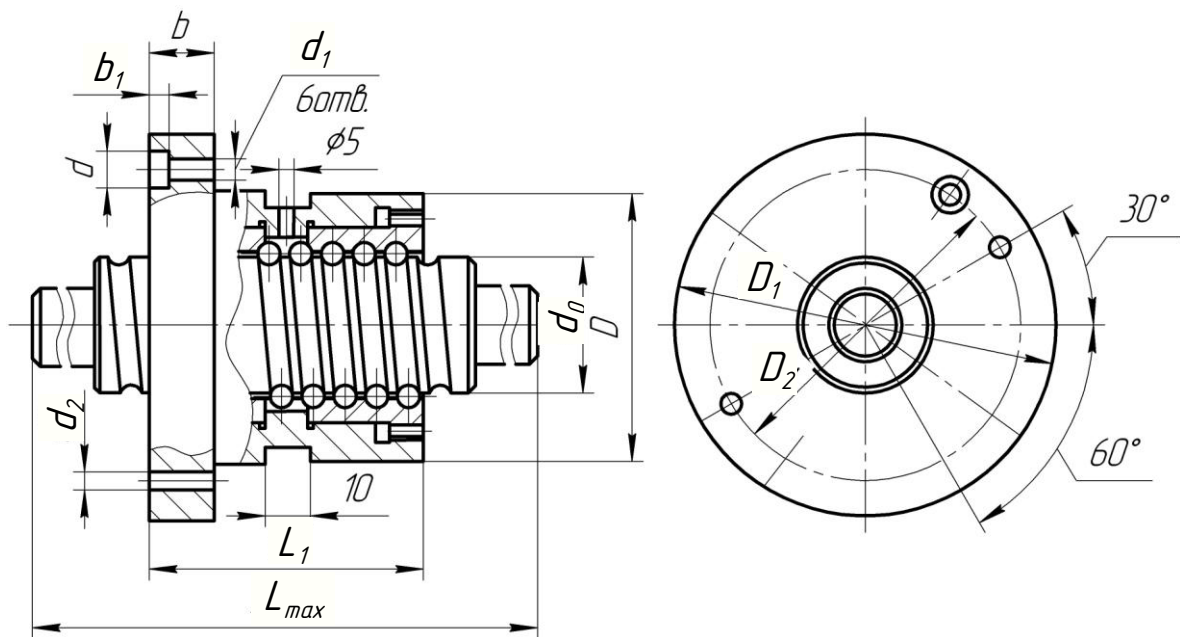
Конструкція та основні розміри кулькової передачі з двома гайками
